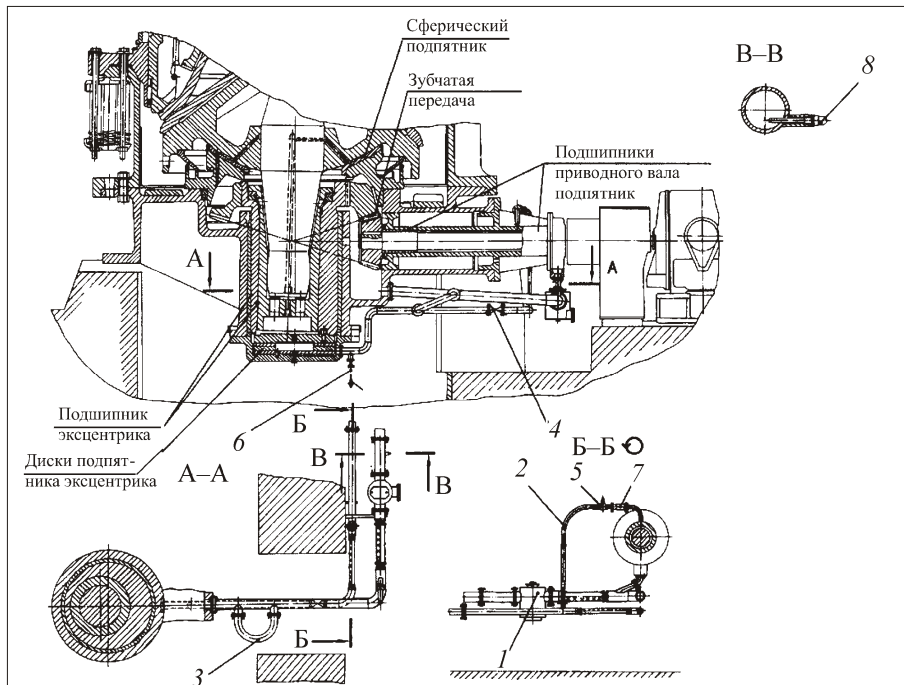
Разводка смазки по дробилке КСД-КМД:
